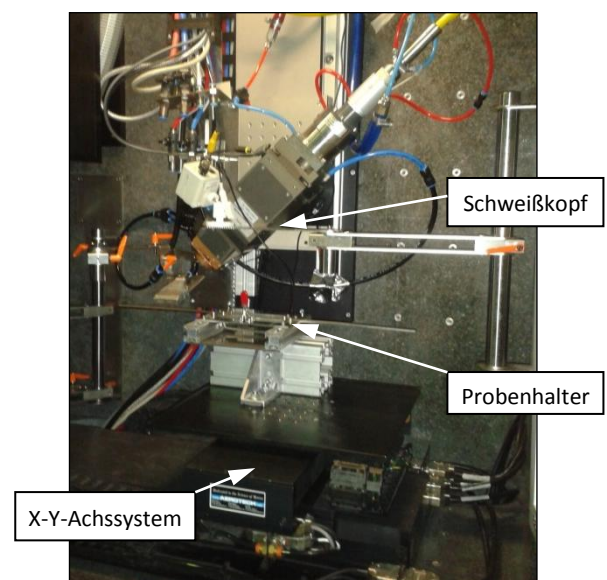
Experimenteller Aufbau für das Laserstrahlschweißen mit Linearmotor- Achssystem und schräg gestelltem Schweißkopf
